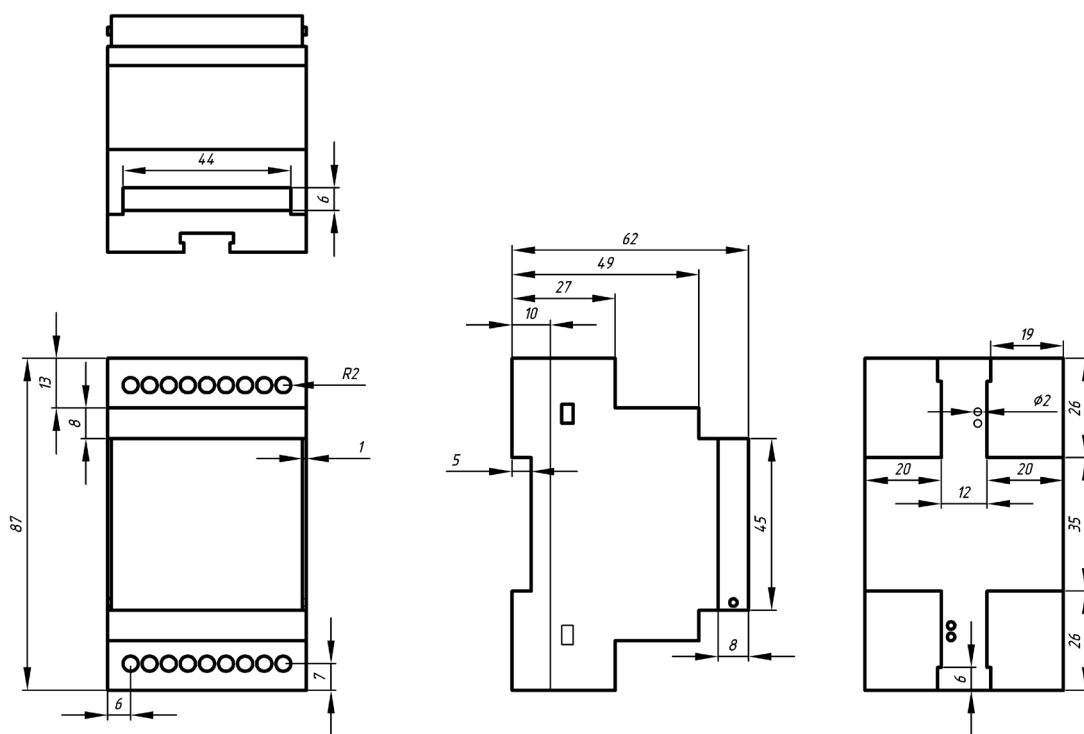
Габаритные размеры БПП в малогабаритном корпусе.
